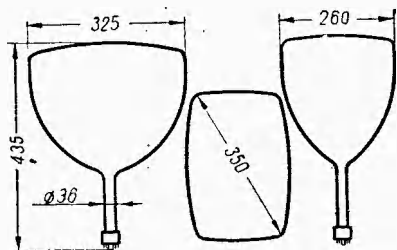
Основные размеры кинескопа 35ЛК2Б.
